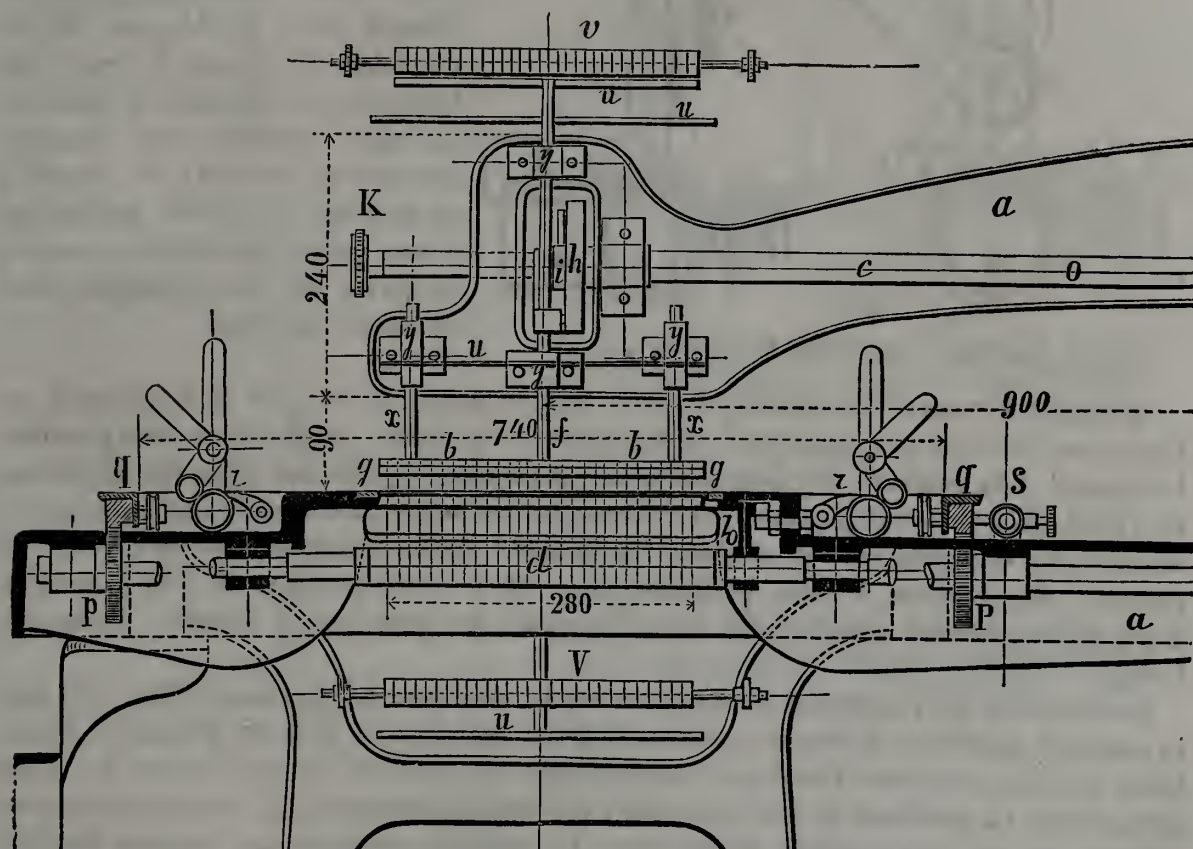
Machine à ouater de MM. Hurtu et Hautin.
